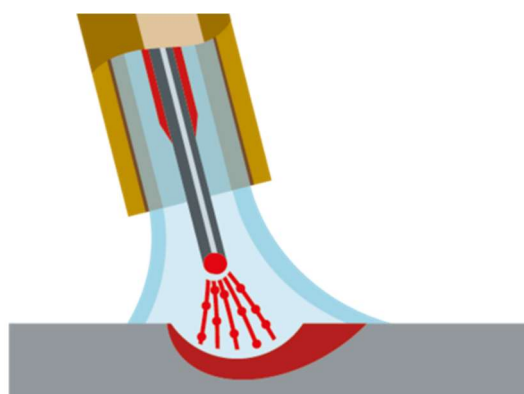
Soldadura MIG (Font: Lorch)
